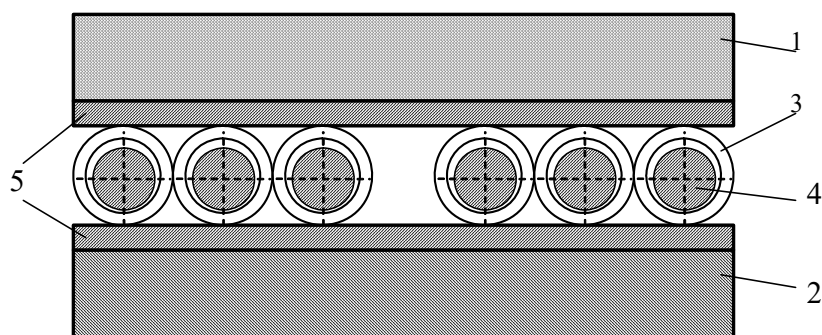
Ескіз паяного з'єднання кераміки з металом: 1 – кераміка;
